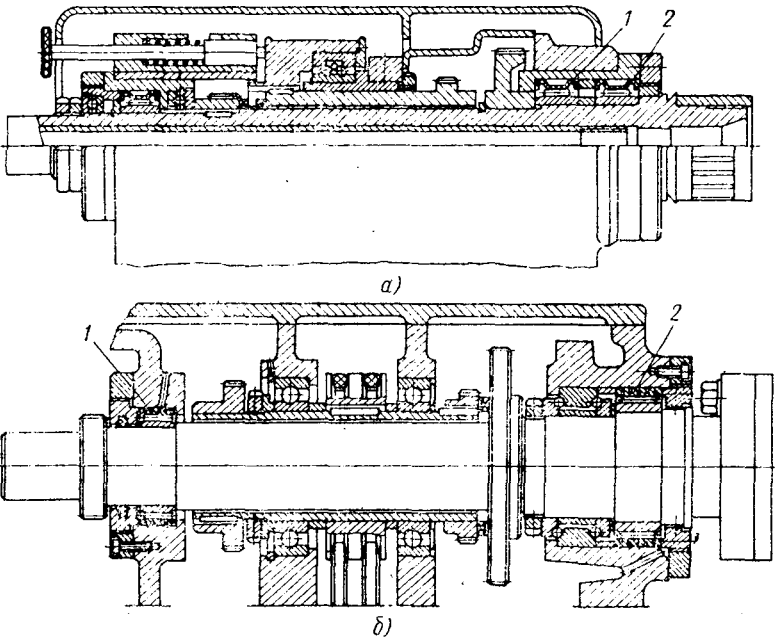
Шпиндельные опоры на игольчатых подшипниках:
